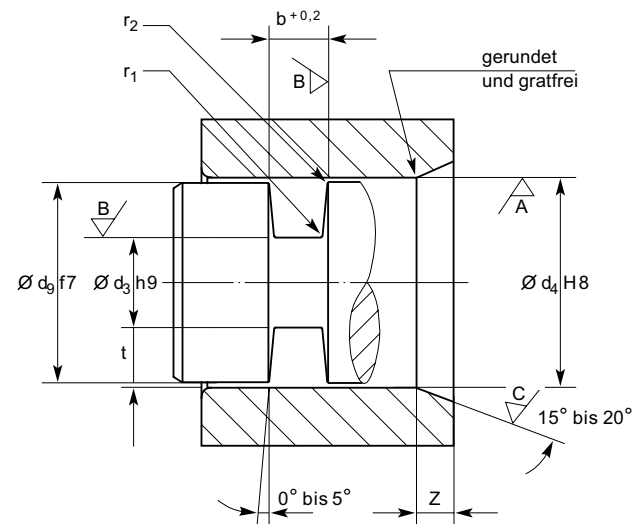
Kolbendichtung – Hydraulik und Pneumatik
